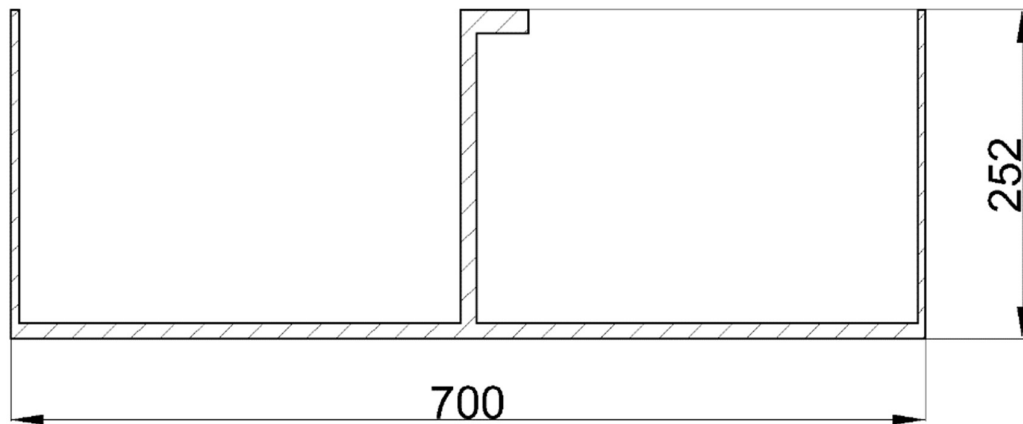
Наближений переріз профілю шпангоута з приєднаним пояском для вихідного варіанта конструкції борту
